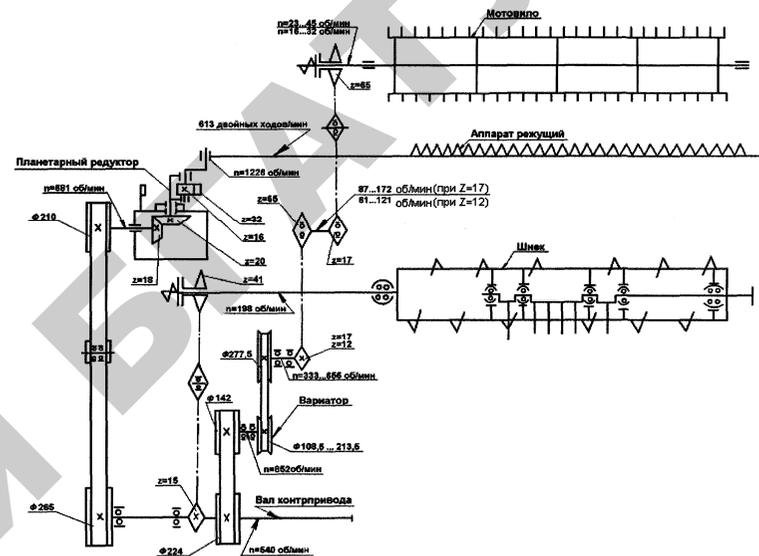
Схема кинематическая жатки ЖЗК-6-1
